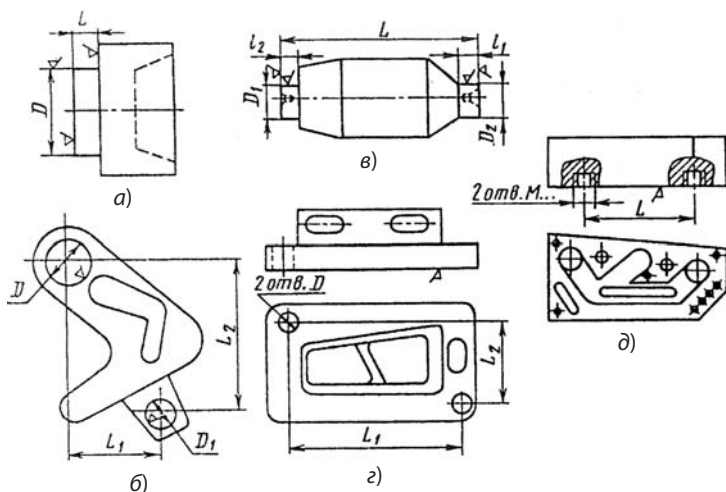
Примеры заготовок с базовыми поверхностями, подготовленными для обработки на станках с ЧПУ
